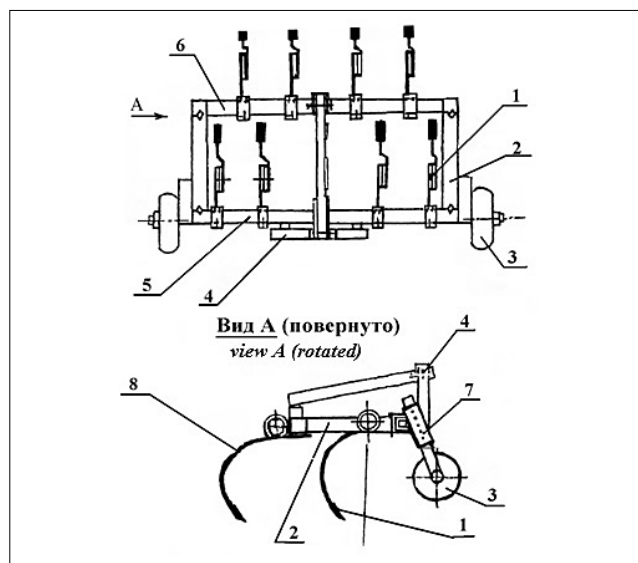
Культиватор чизельный горный КЧГ-2,4: 1 – рабочий орган; 2 – балка поперечная; 3 – опорное колесо; 4 – автосцепка СА-2; 5 – передняя балка рамы; 6 – задняя балка рамы; 7 – телескопическое соединение регулировки глубины обработки; 8 – стойка рабочего органа
